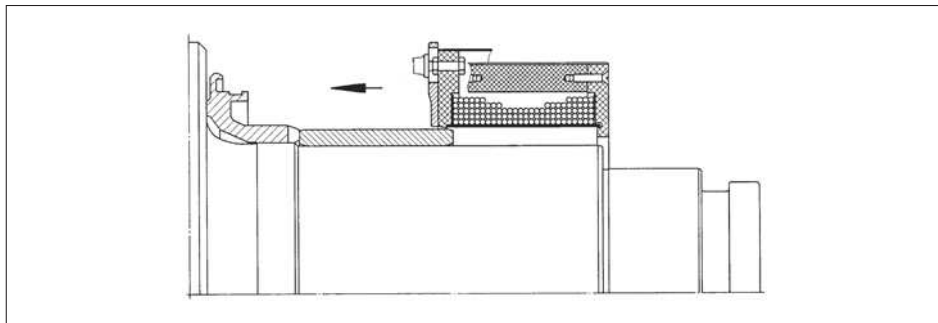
O aquecedor está sendo posicionado sobre o anel
